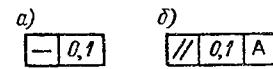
Нанесение обозначения допусков в рамке
